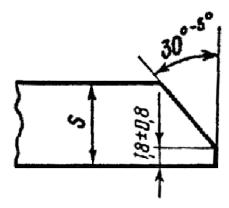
Разделка кромок под сварку, S=12 мм.
